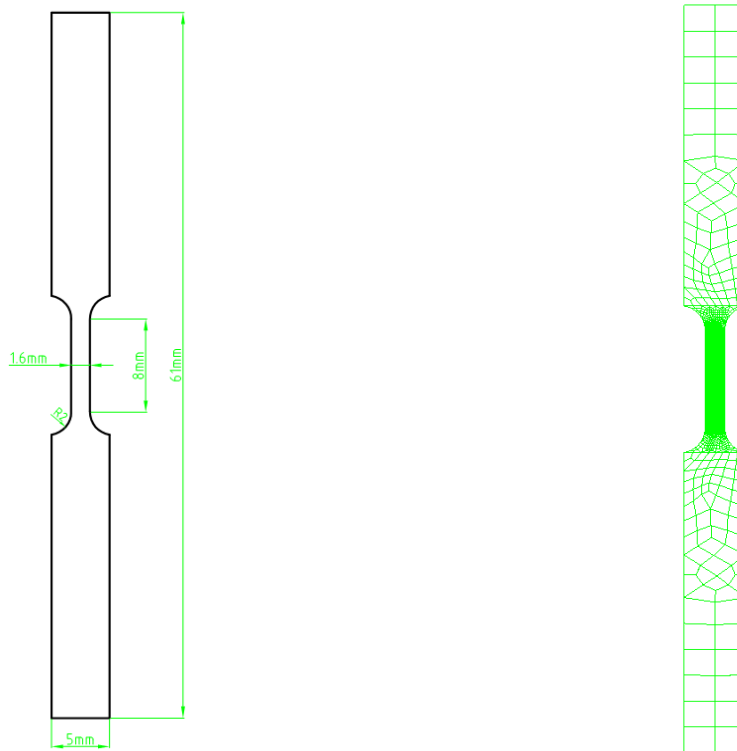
Novo provete de tracção em estado plano de deformação. a) Geometria do provete; b) Malha de elementos finitos com 3714 elementos (Teng, 2008).
